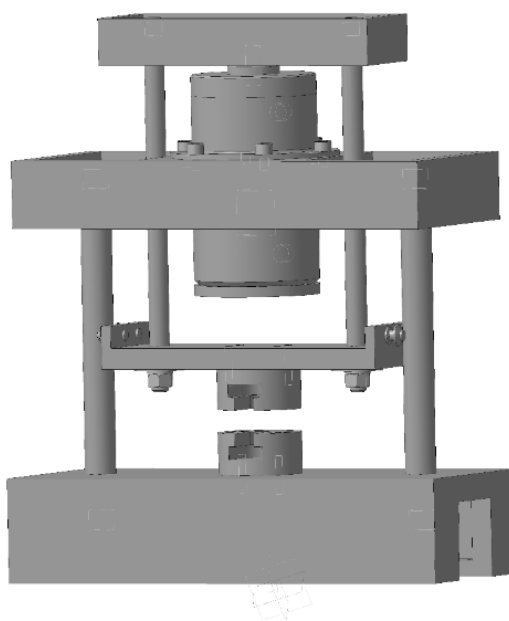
3D модель приспособления для растяжения цилиндрических образцов с буртиками
